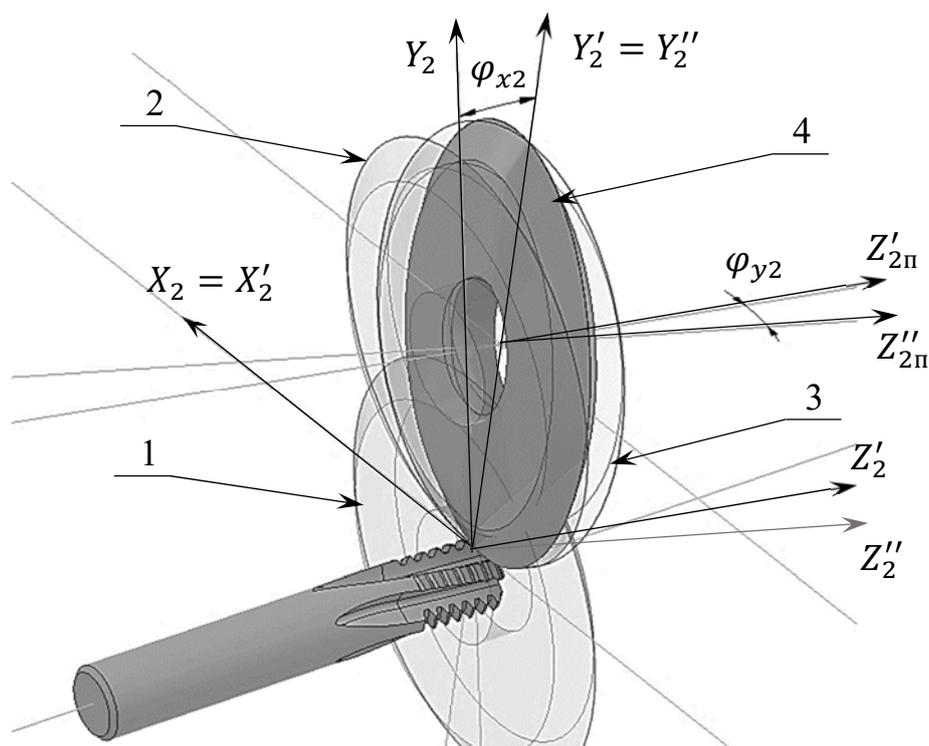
Последовательность установки шлифовального круга на зуб резбовой фрезы. (1 – начальное расчётное положение шлифовального круга, 2 – установка шлифовального круга на зуб, 3 – поворот шлифовального круга на угол φ_{x2} , 4 – поворот шлифовального круга на угол φ_{y2}). $Z'_{2п}$ и $Z''_{2п}$ - перенесенные к центру шлифовального круга оси Z'_2 и Z''_2 соответственно.
